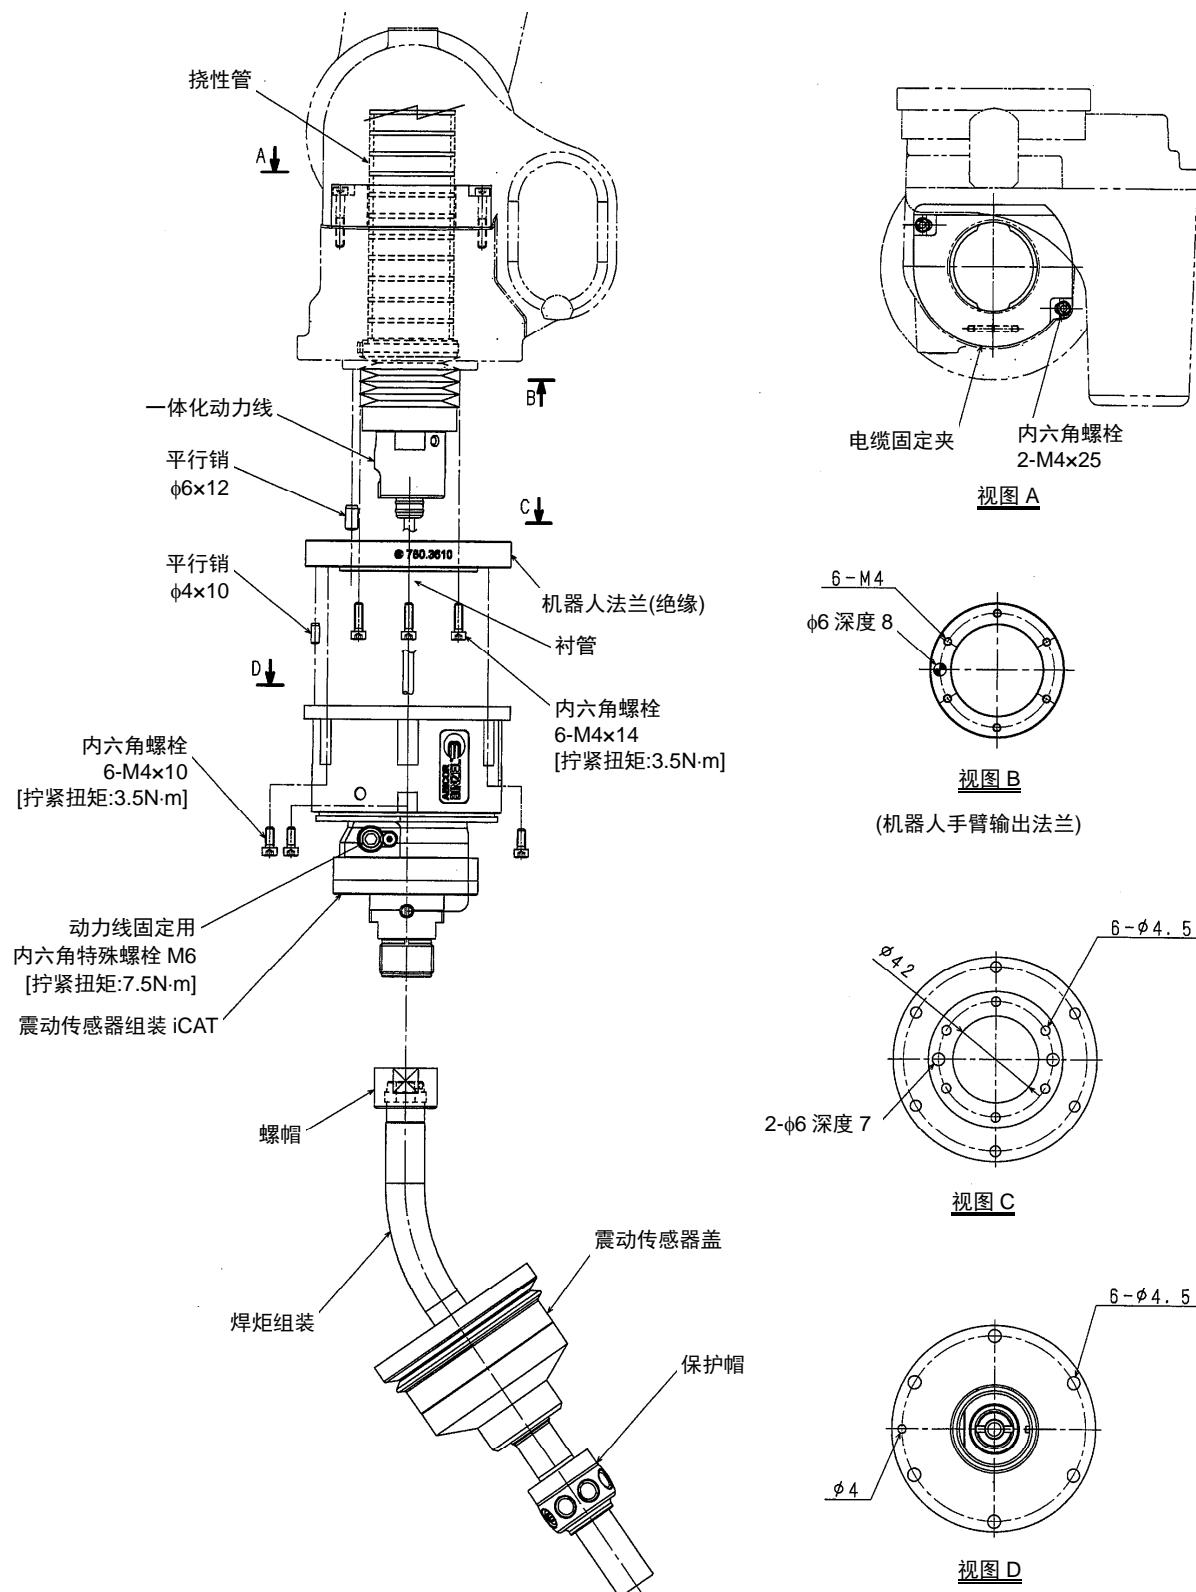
BINZEL 公司生产的焊炬及震动传感器的安装
